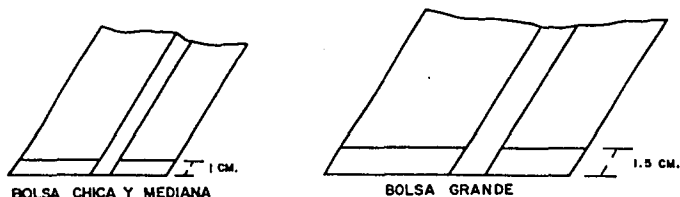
DIMENSIONES DEL CIERRE CORRUGADO.
